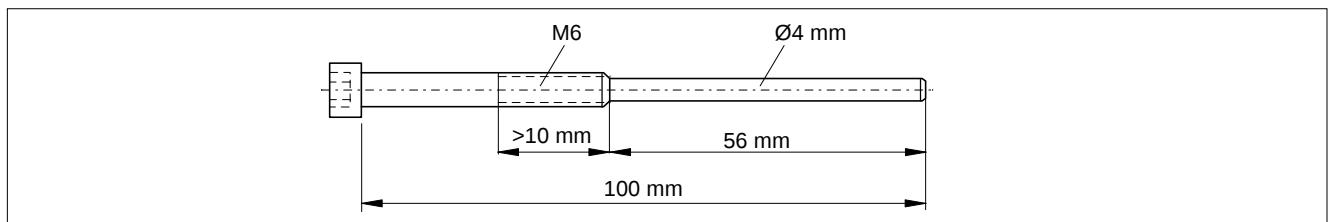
Sonderschraube für Demontage ERN 1387 und EQN 1325
